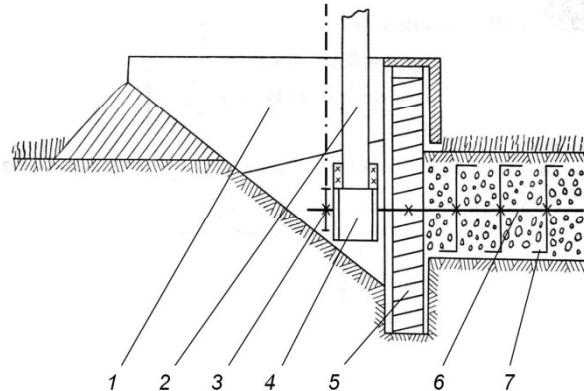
Устройство для обработки почвы с открытым редуктором: 1 — отвальный элемент; 2 — стойка; 3 — цепная передача; 4 — опора вала; 5 — роторный щелерез; 6 — вал фрезерователя; 7 — фреза
